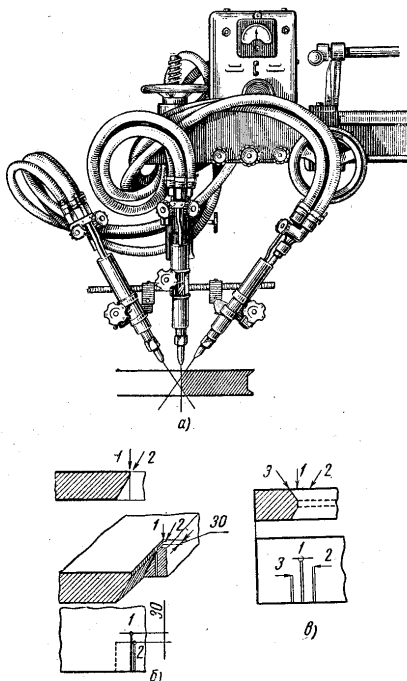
Резка кромок несколькими резаками одновременно:
